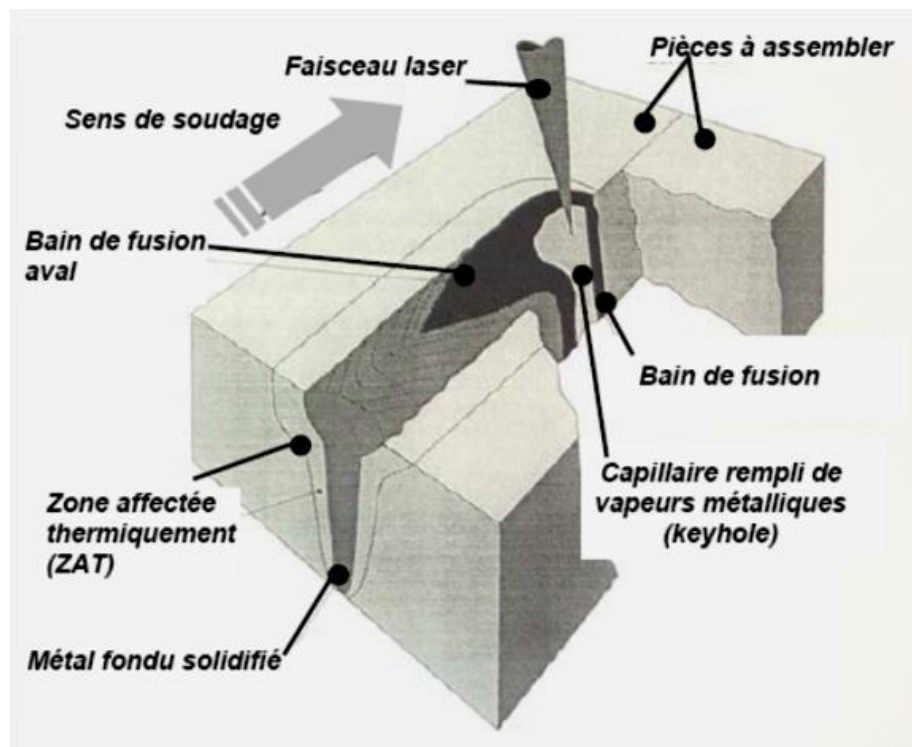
Soudage laser par Keyhole [21].
